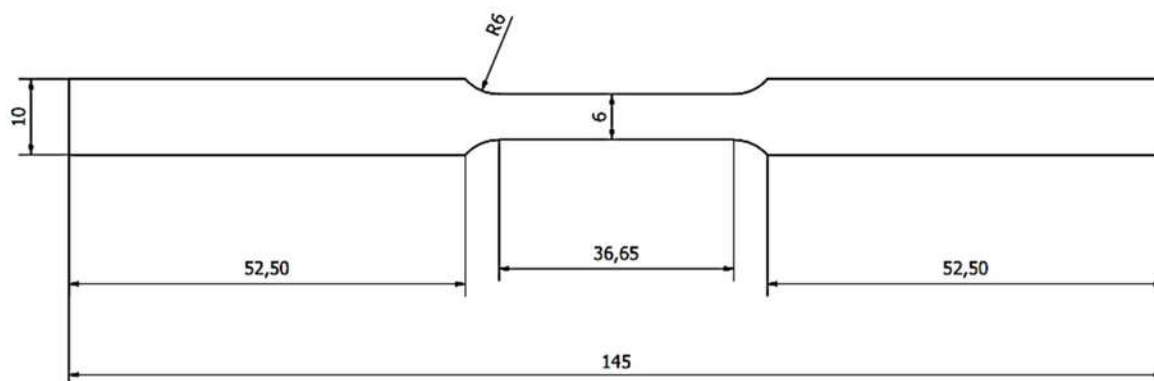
Geometría de las probetas para ensayo de tensión uniaxial, dimensiones en mm.
